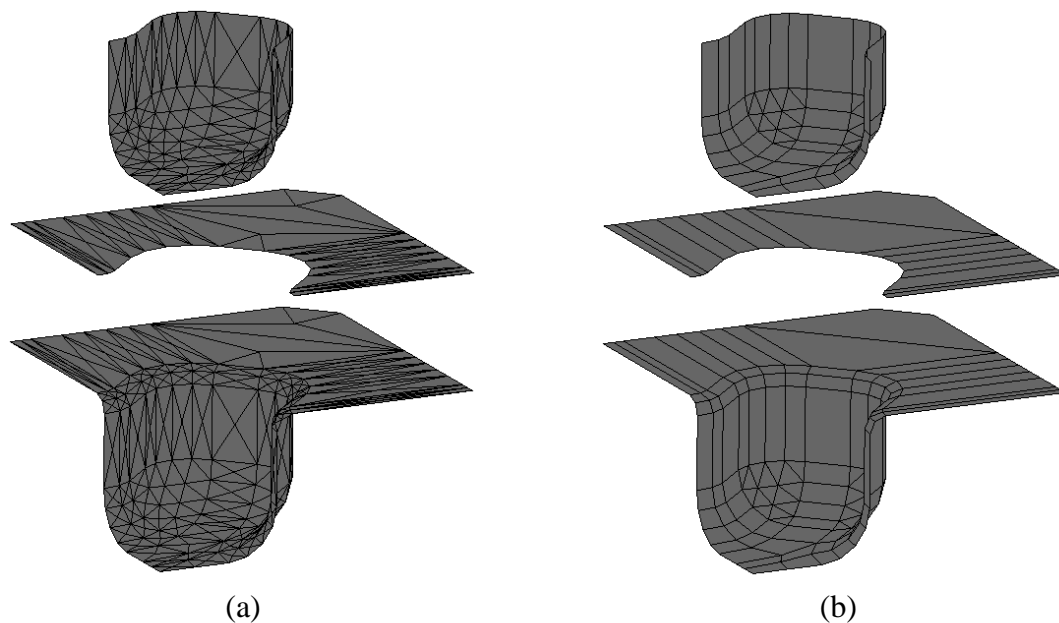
Discretizações estruturadas utilizadas na construção dos modelos: (a) E-388; (b) E-226.
